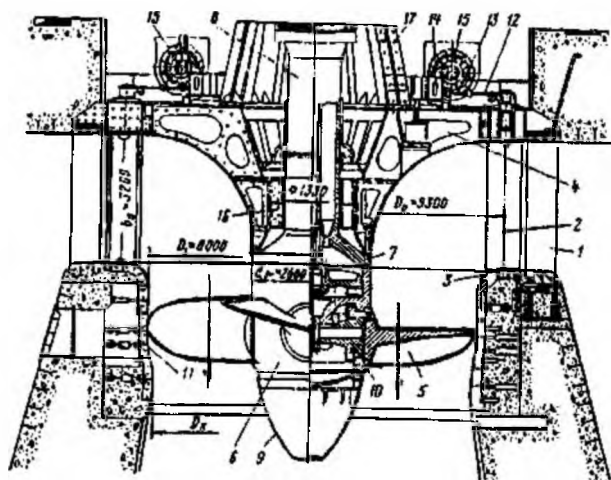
Осевая поворотная-лопастная турбина, установленная на Кременчугской ГЭС: 1 – колонны статора; 2 – направляющие лопатки; 3 – нижнее кольцо; 4 – крышка турбины; 5 – лопасти рабочего колеса; 6 – втулка; 7 – фланец вала; 8 – вал; 9 – обтекатель рабочего колеса; 10 – камера рабочего колеса; 11 – выдвижной сегмент; 12 – рычаг направляющей лопатки; 13 – серья; 14 – регулирующее кольцо; 15 – сервомоторы; 16 – подшипник; 17 – опорная конструкция подпятника генератора
